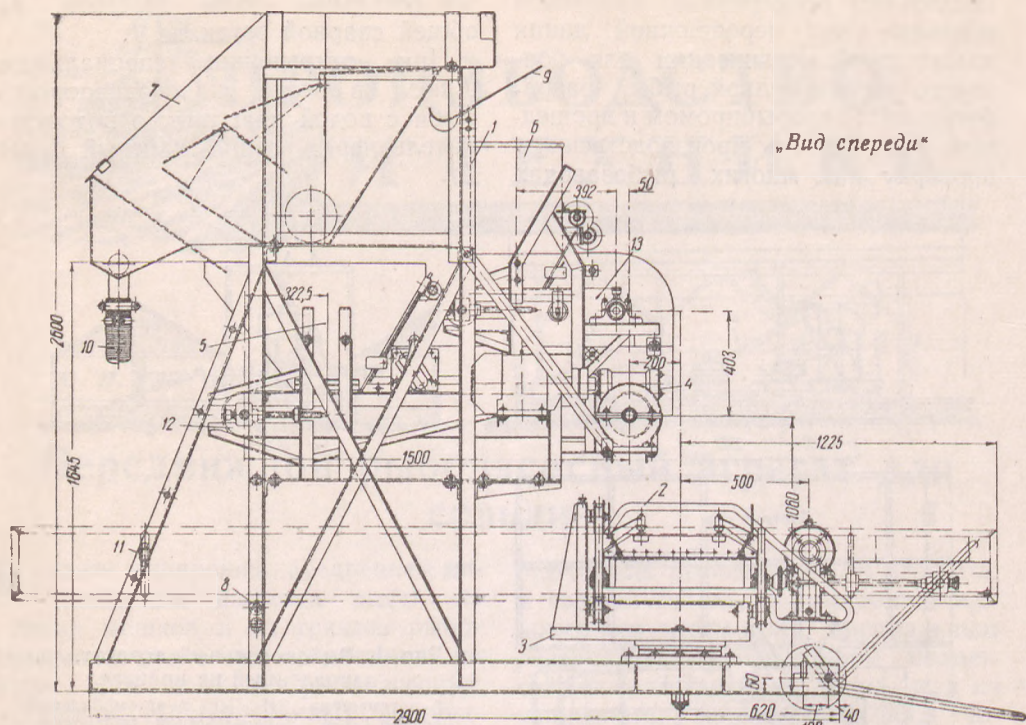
Общий вид передвижного рыбопосольного агрегата:
